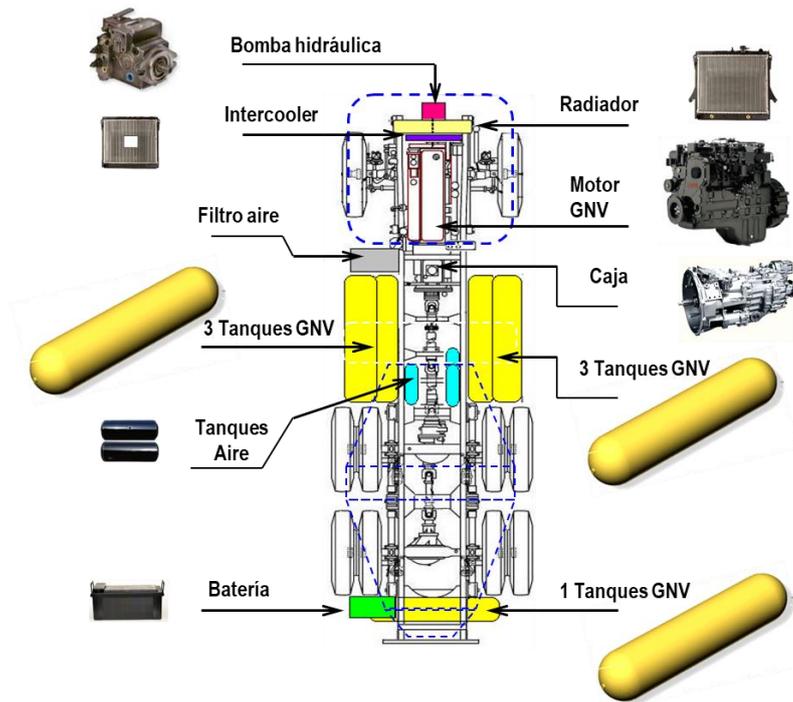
Partes del camión con el Motor GNV y los Tanques Instalados.
